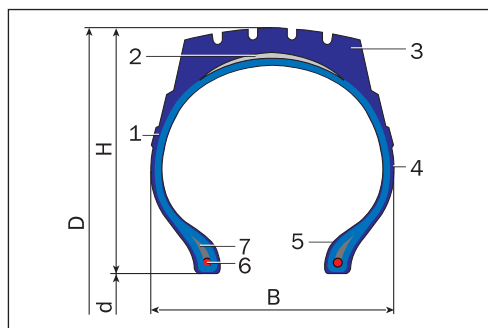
Конструктивные элементы и основные размеры шины: D — наружный диаметр; H — высота профиля шины; B — ширина профиля шины; d — посадочный диаметр обода колеса (шины); 1 — каркас; 2 — брекер; 3 — протектор; 4 — боковина; 5 — борт; 6 — бортовая проволока; 7 — наполнительный шнур
